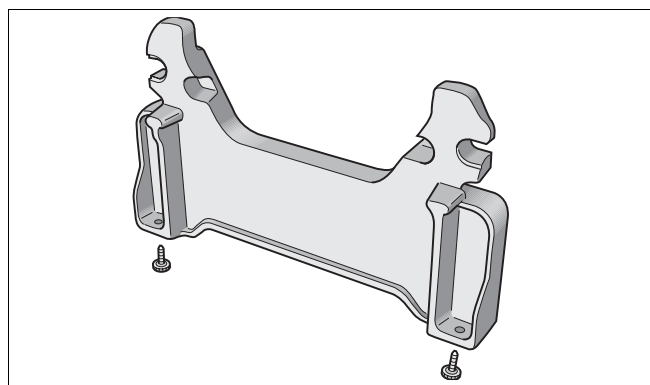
Monter les pieds réglables sur le socle de la chaudière (hauteur 140 mm)
